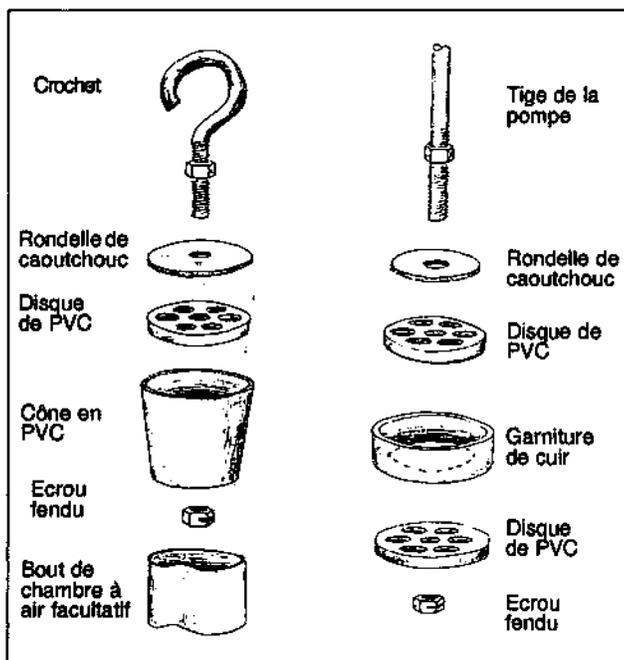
Dessin éclaté du clapet de pied et du piston proprement dit.
